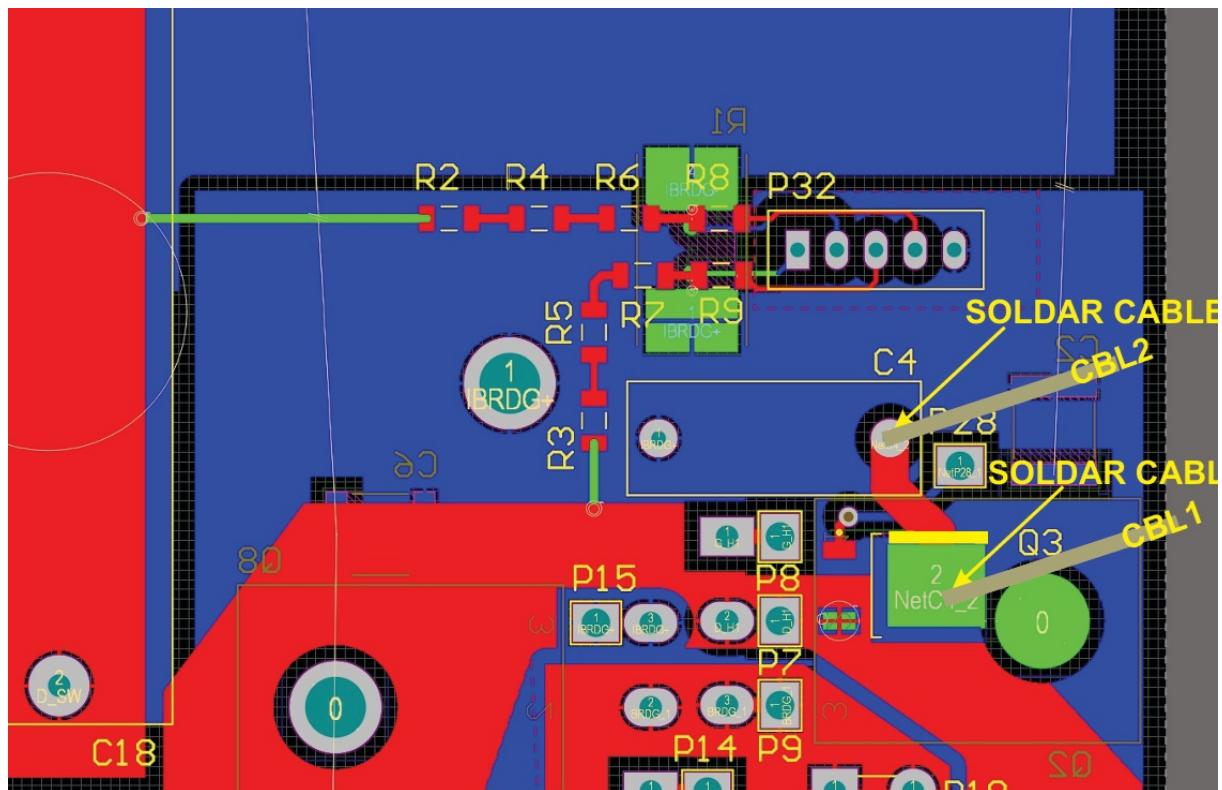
Conexionado de los cables CBL1 y CBL2 para una red Snubber.
